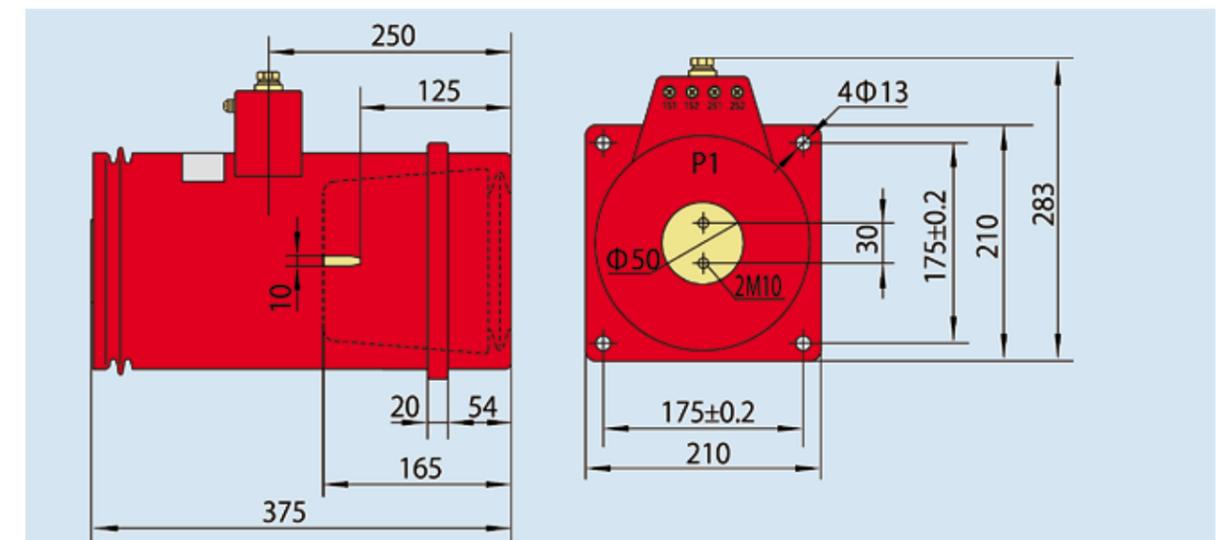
Внешний вид и размеры при 300-600/5 А
